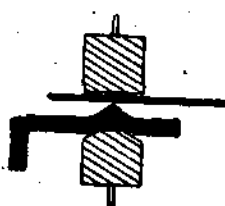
Подготовка к сварке при неравной толщине свариваемых деталей.
